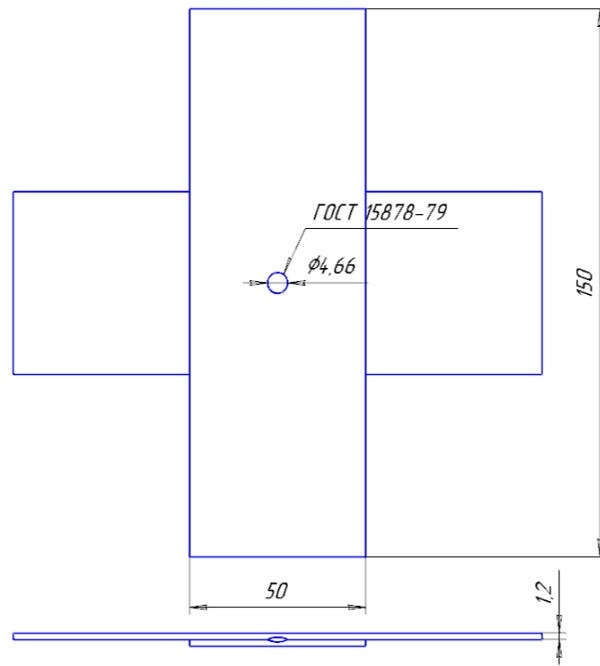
Образец для испытаний на отрыв сварной точки
